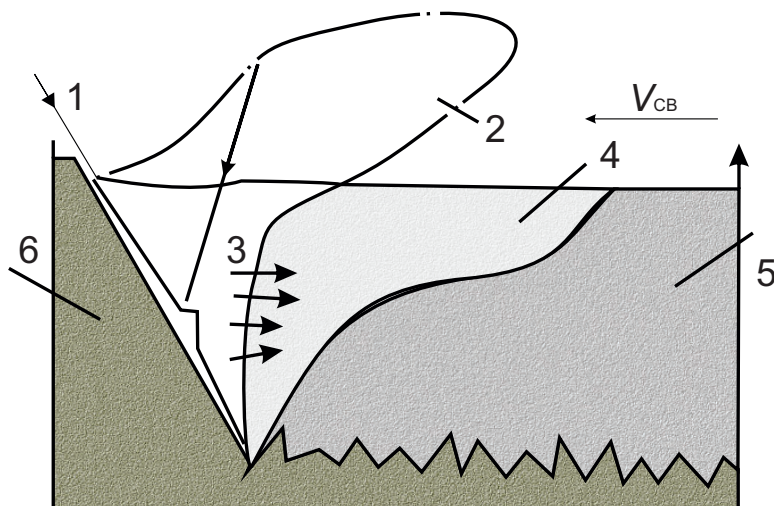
Схема продольного сечения сварочной ванны:
